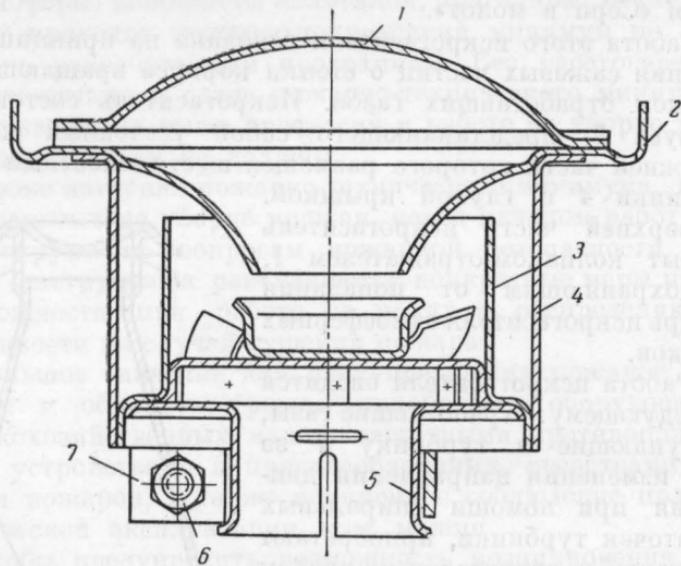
Центробежный искрогаситель-глушитель Минского тракторного завода:
